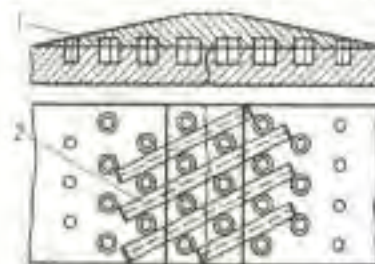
Схема розташування сталевих зв'язок у металі шва при холодному зварюванні чавуну: 1 – шпильки; 2 – сталеві зв'язки
